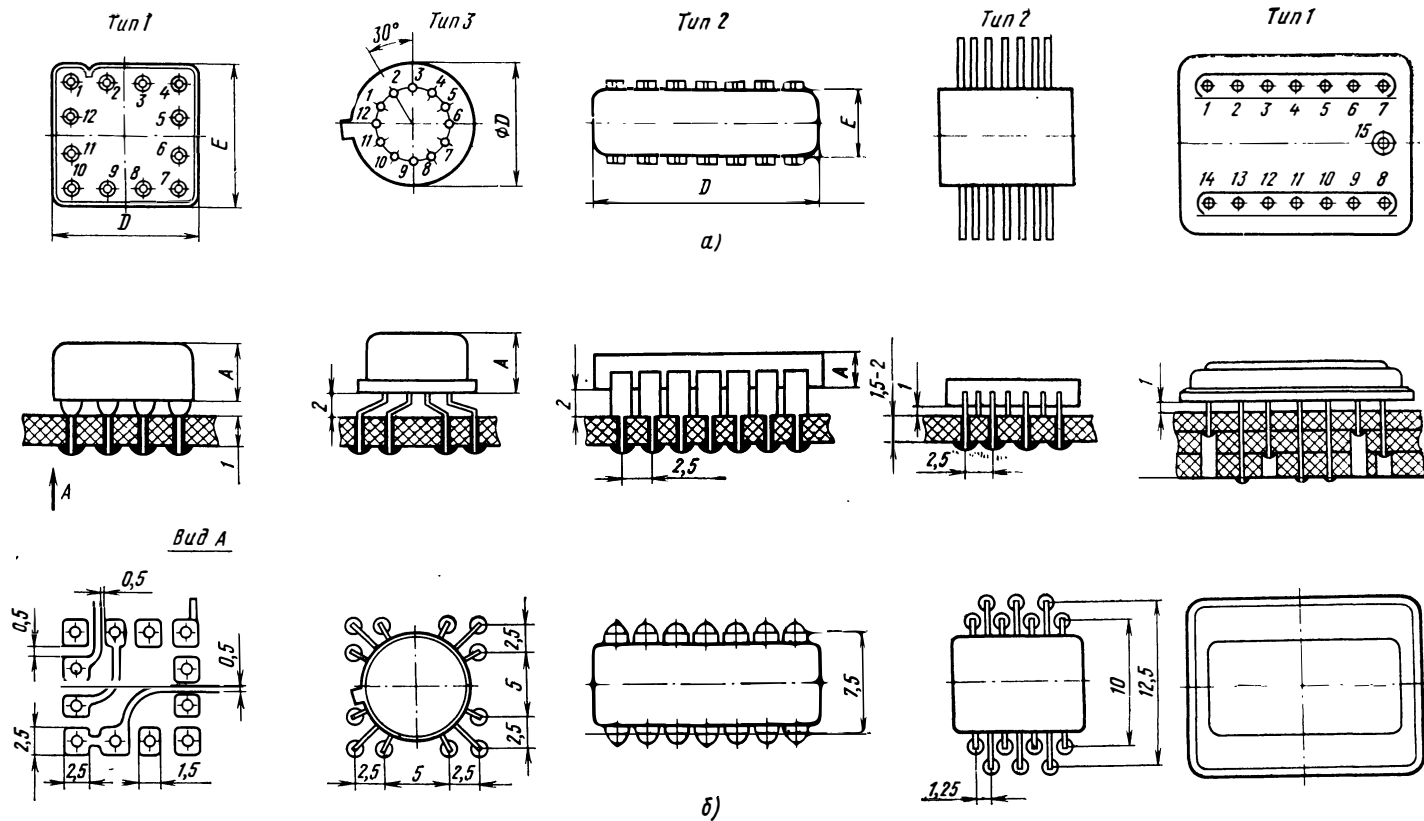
Микросхемы в типовых корпусах (а) и примеры установки их на печатных платах (б)
